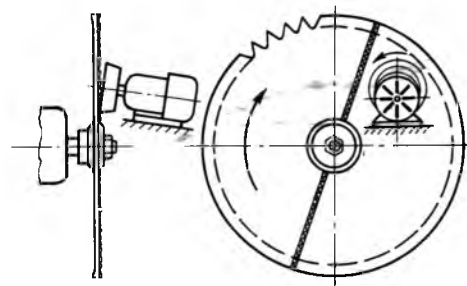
Схема зачистки шва сварной дисковой пилы
